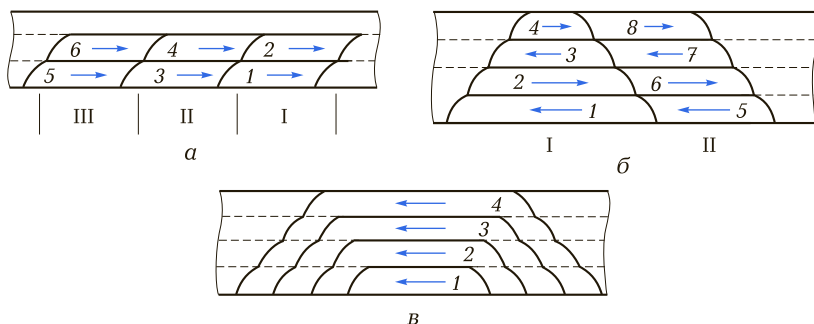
Сварка металлических частей большой толщины:
